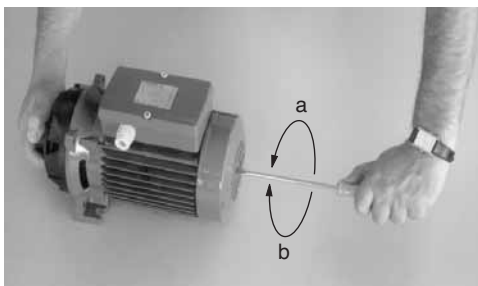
Снятие (а) и повторная установка (b) рабочего колеса
